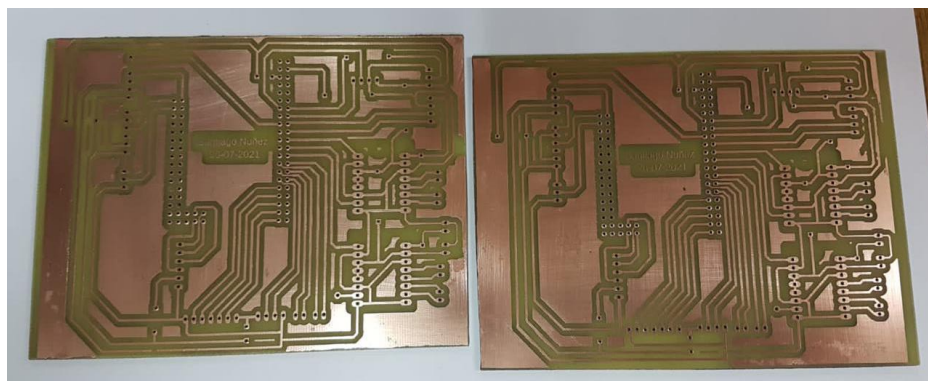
Placas construidas para el funcionamiento de Arduino mega Embed, Nano y Puentes H
